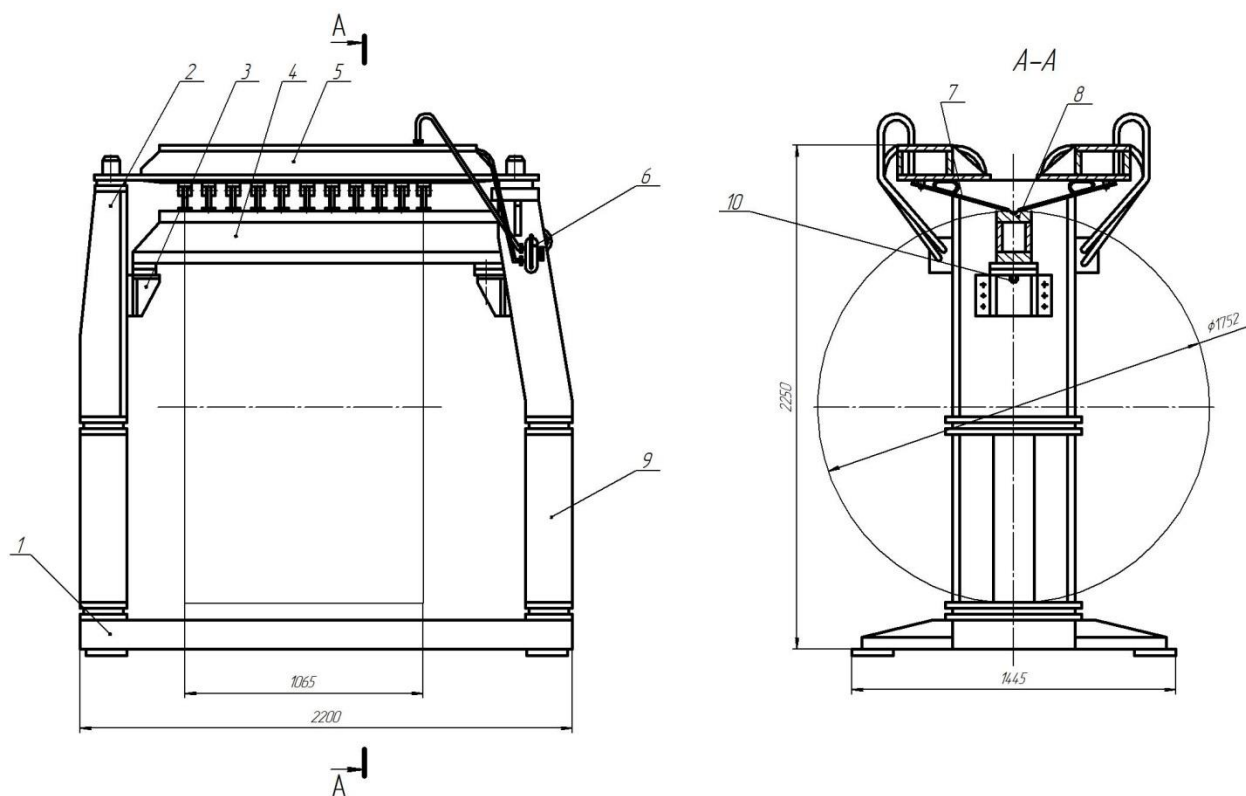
Сборочное приспособление для выполнения продольного шва на обечайках
